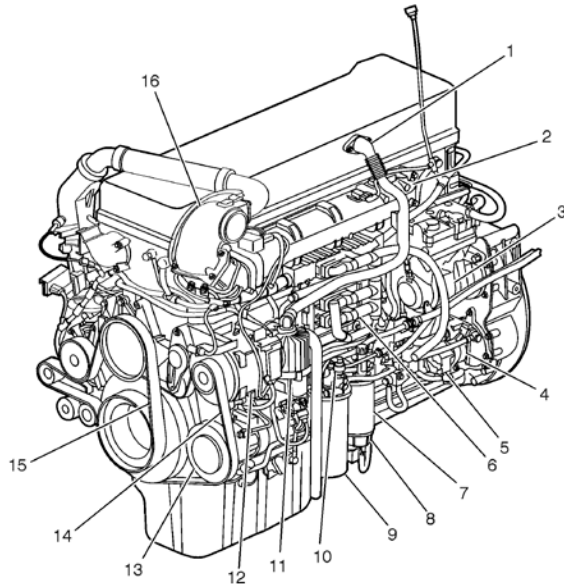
VUE D'ENSEMBLE DU MOTEUR D13H, CÔTÉ ALTERNATEUR (TYPIQUE)
